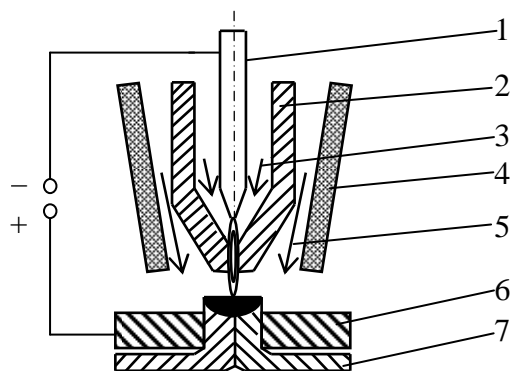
Микроплазменная горелка: 1 – электрод; 2 – сопло; 3, 5 – плазмообразующий и защитный газы; 4 – корпус плазмотрона; 6 – теплоотвод; 7 – фланцы корпуса микросхемы
